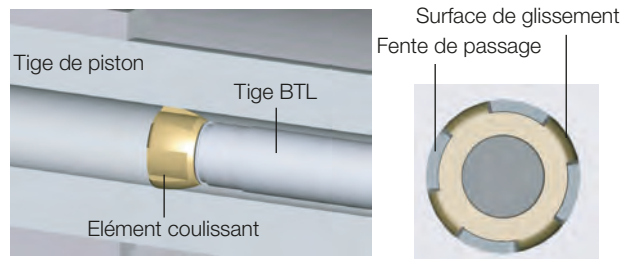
Vue détaillée et vue de dessus de l'élément coulissant
